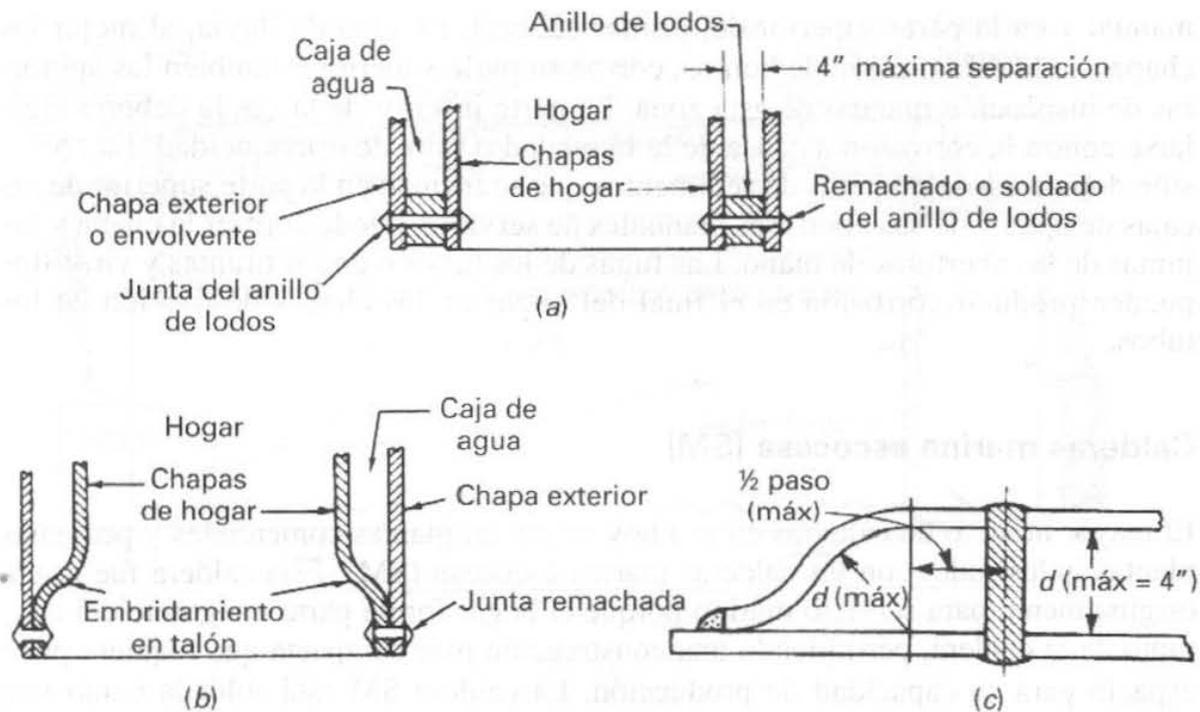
Detalles constructivos de la parte interior de las cajas de agua. (a) Cierre tipo anillo de lodos. (b) Brida en talón roblonada. (c) Cierre embrindado en talón con soldadura.
